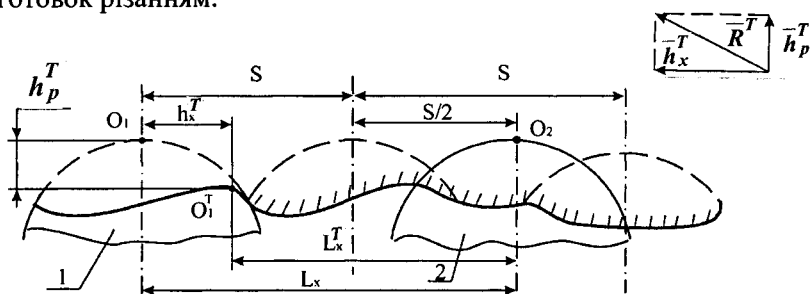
Схема формування складових вектора розузгодження стану вершин різців.
